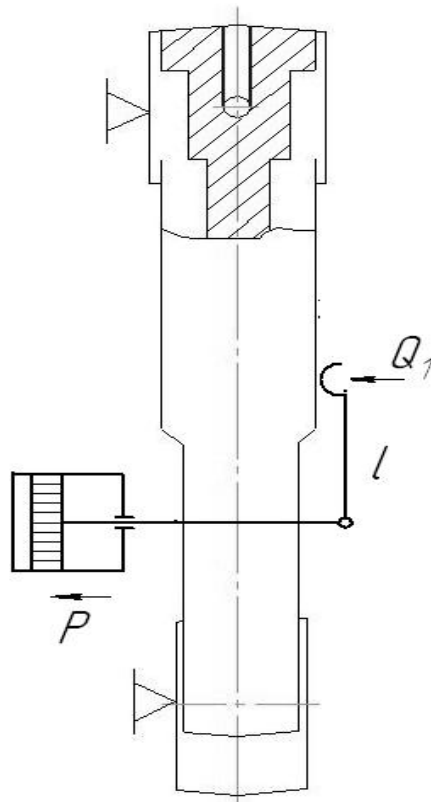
Схема закріплення заготовки у свердлильному пристосуванні
